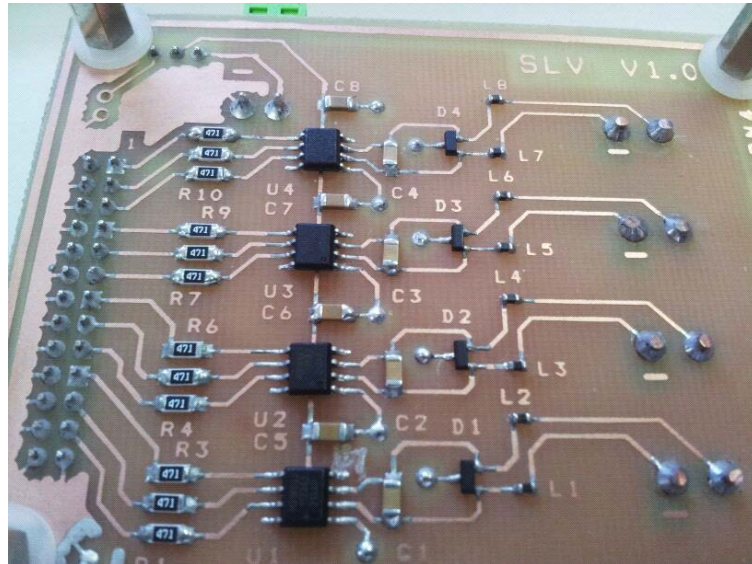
Placa acondicionadora finalizada. Detalle de soldaduras.
